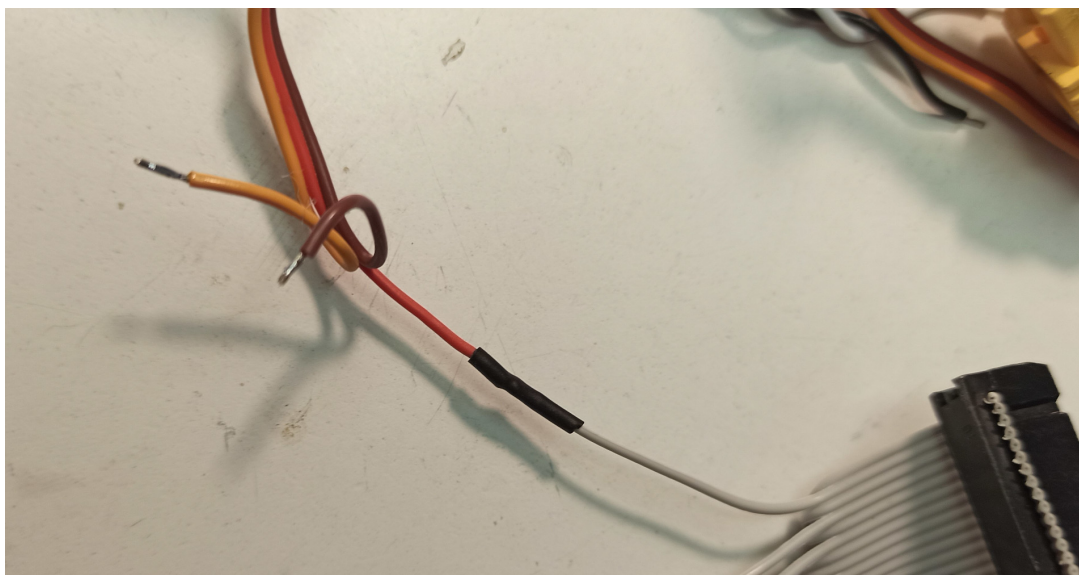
Soldatge dels cable dels ESCs amb el connector IDC
